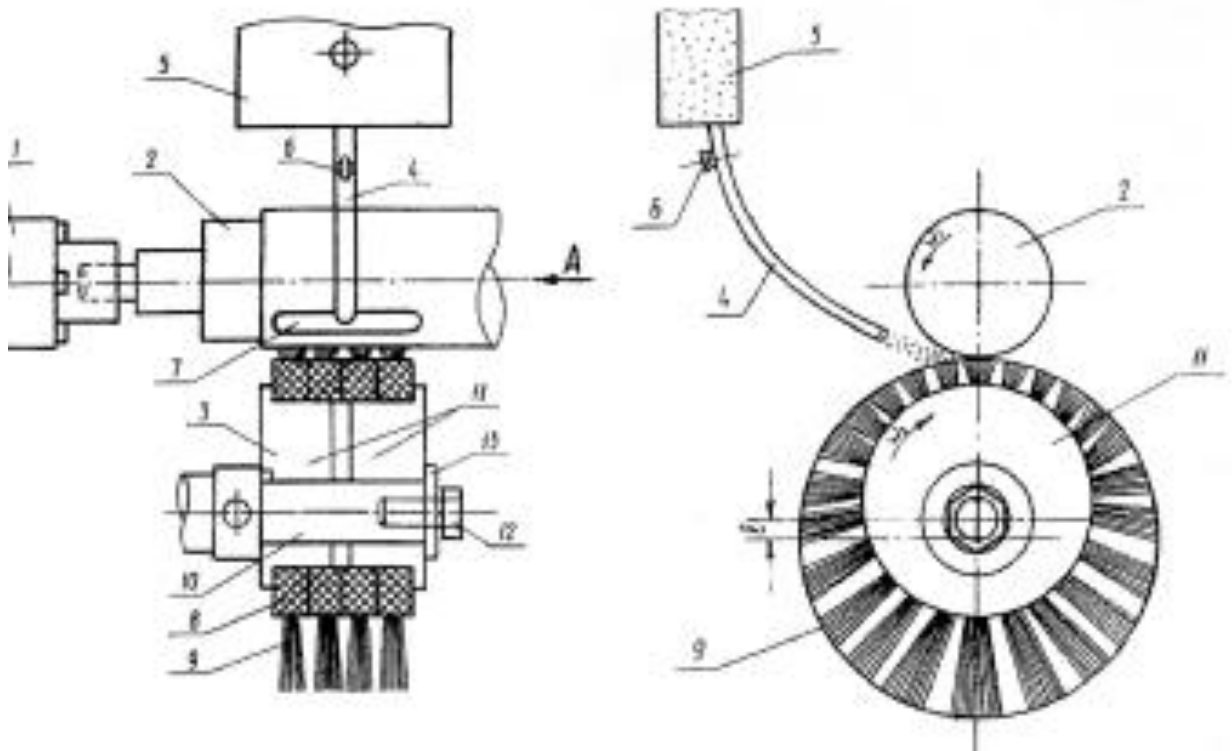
Эскиз приспособления для притирки поверхности деталей
